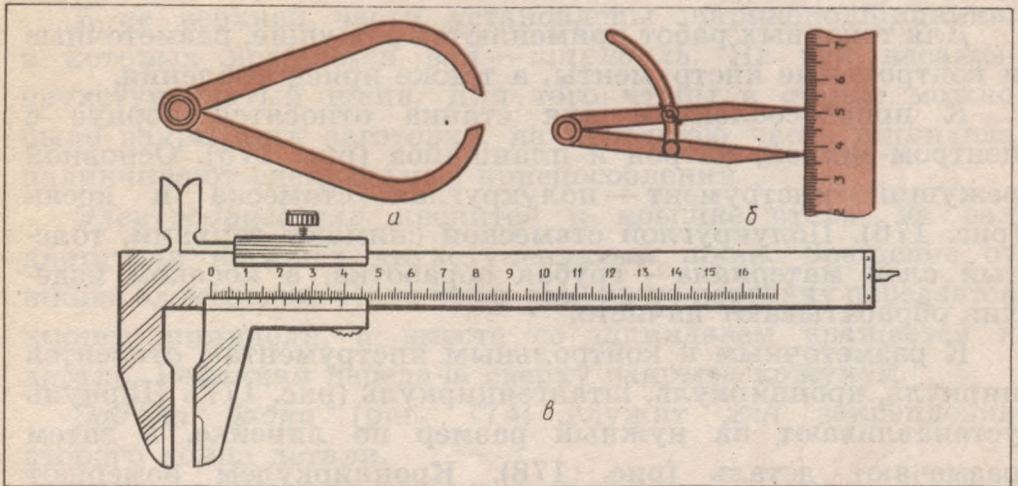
Разметочные, измерительные и контрольные инструменты для токарных работ: *а* — кронциркуль; *б* — циркуль; *в* — штангенциркуль.
